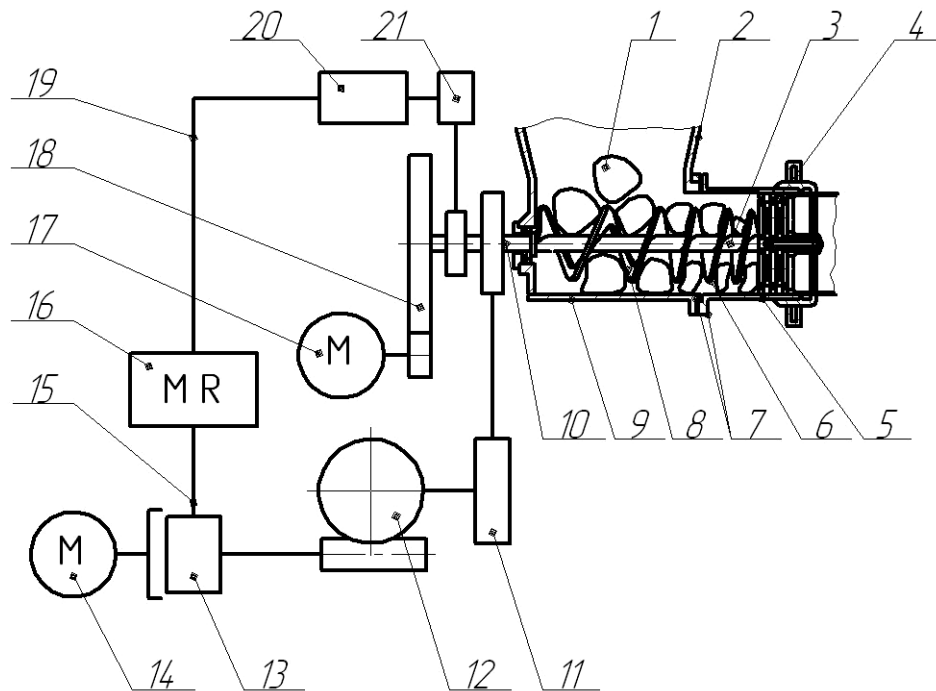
Схема автоматичного регулювання транспортування м'яса до зони подрібнення: 1 - сировина; 2 - завантажувальний бункер; 3 - вал; 4 - камера подрібнення; 5,9 - циліндричний корпус; 6 - робочий шнек; 7 - область переходу; 8 - транспортувальний шнек; 10 - порожнистий вал; 11 - клинопасова передача; 12 - редуктор; 13 - муфта вихрового струму; 14,17 - електродвигун; 15 – керуюча шина; 16 – мікро ЕОМ; 18 - зубчаста передача; 19 - сигнальна шина; 20 - тахометр; 21 - сканер кількості обертів
